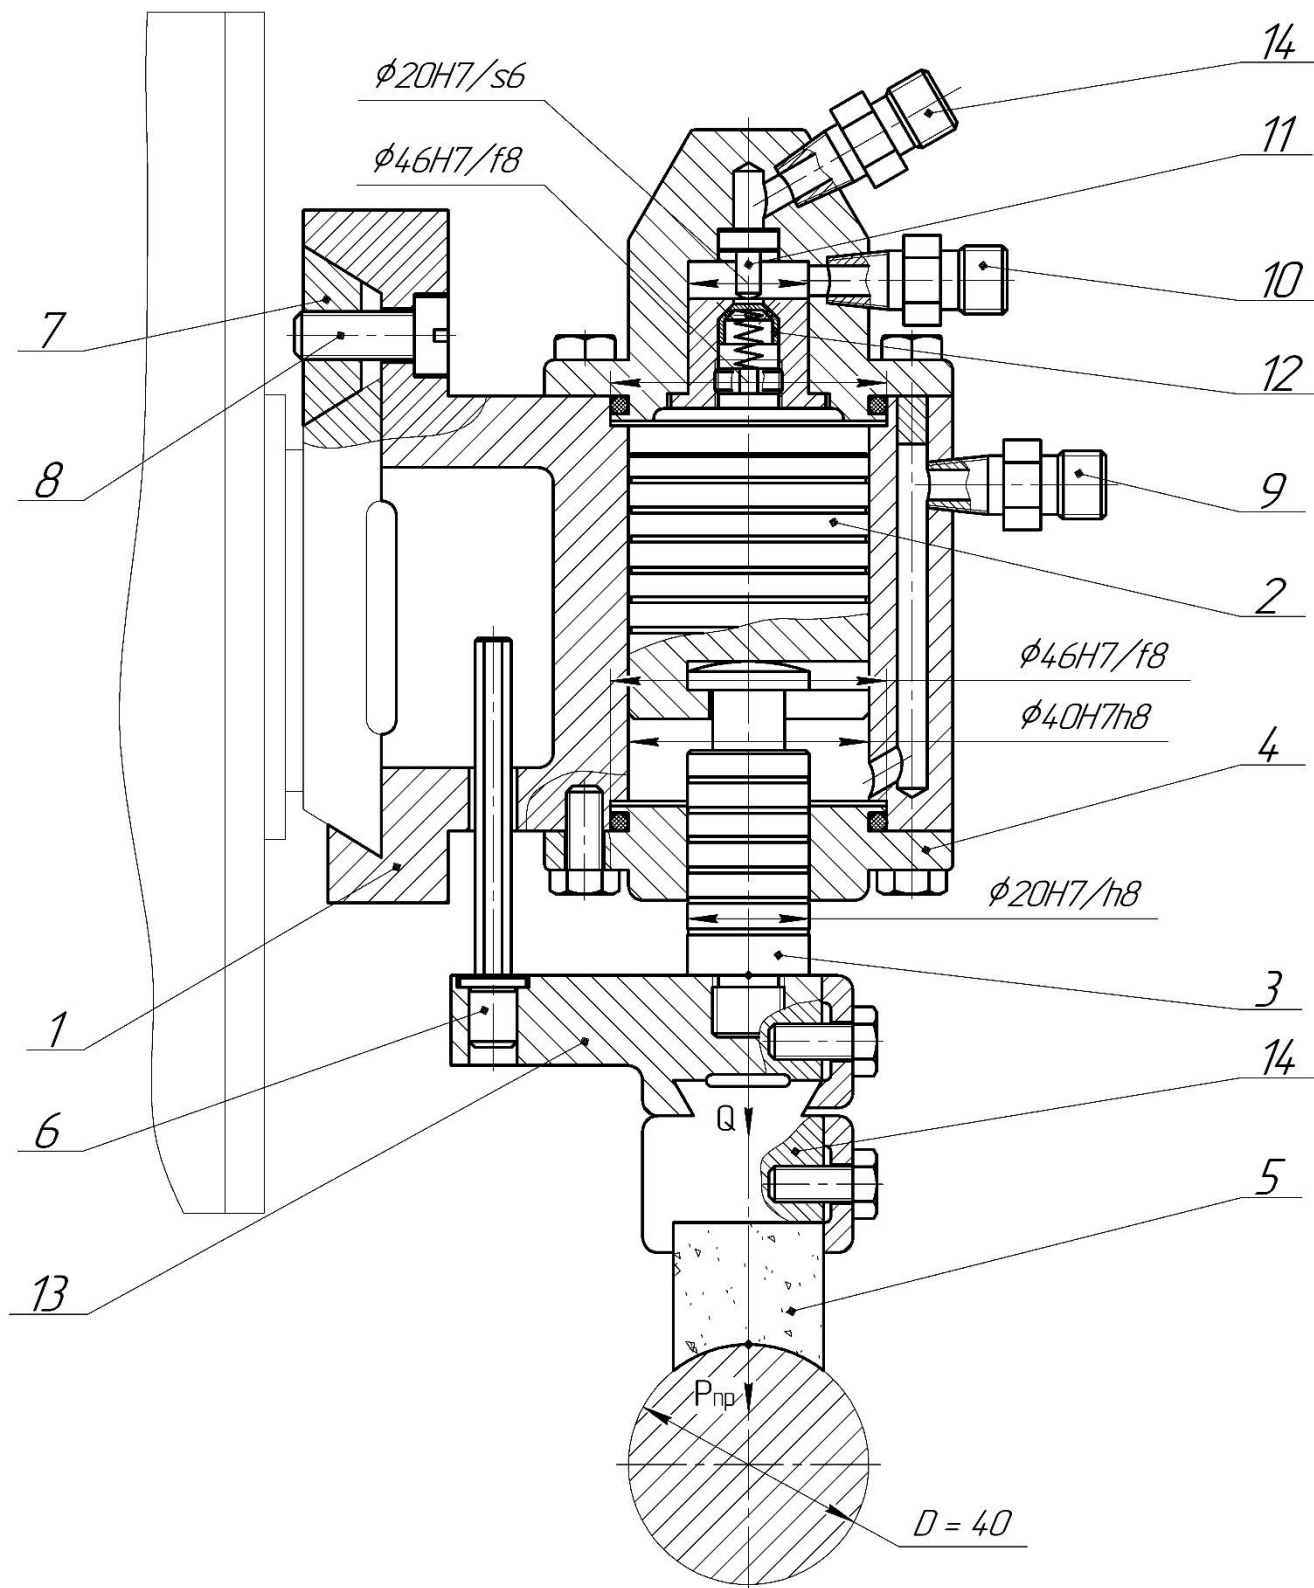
Пристрій для суперфінішування східчастих поверхонь золотника
